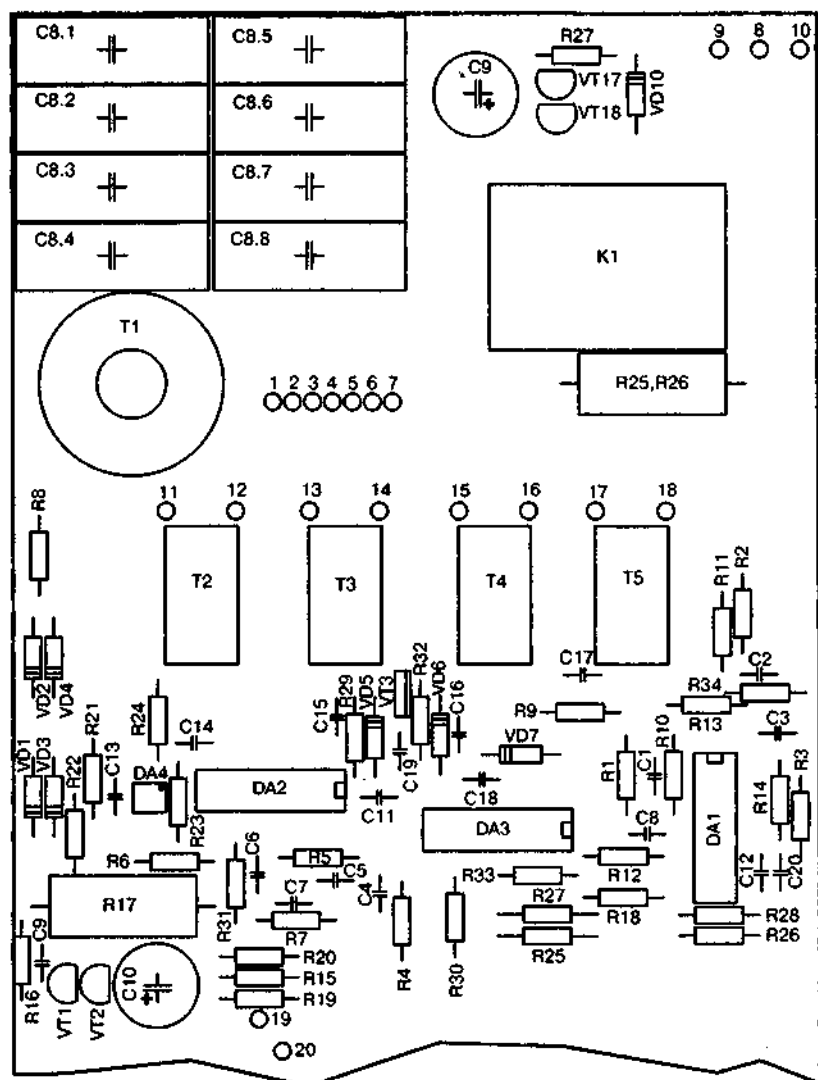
Расположение элементов на плате управления сварочного источника TORUS
